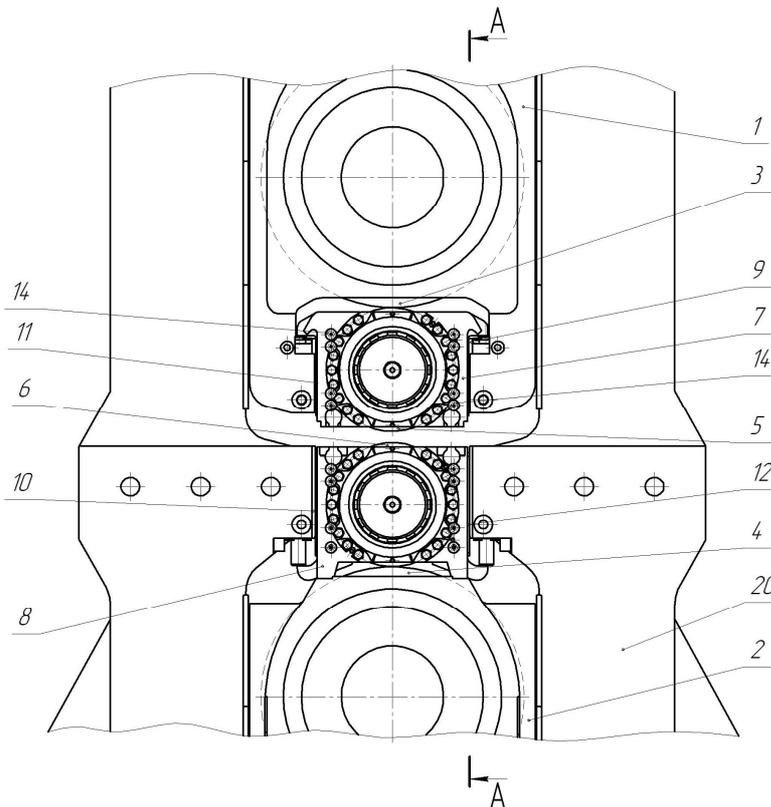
Общий вид черновой прокатной клетки с узлами ГРК со стороны привода
